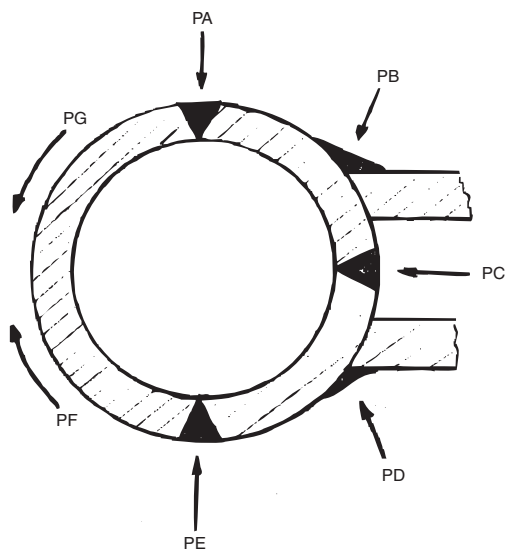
Положения сварных швов согласно ISO 6947
